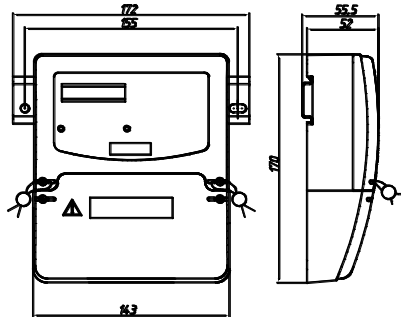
Загальний вигляд лічильника ЦЗ6804-U у корпусі P32
